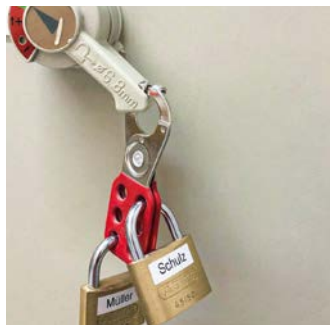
Hauptschalter mit Klaue für mehrere Vorhängeschlösser
